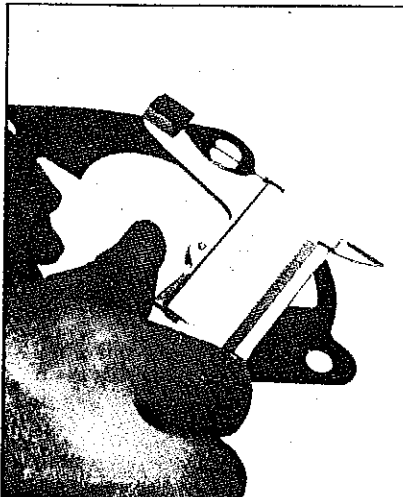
MEDIÇÃO DA JUNTA DO CILINDRO
